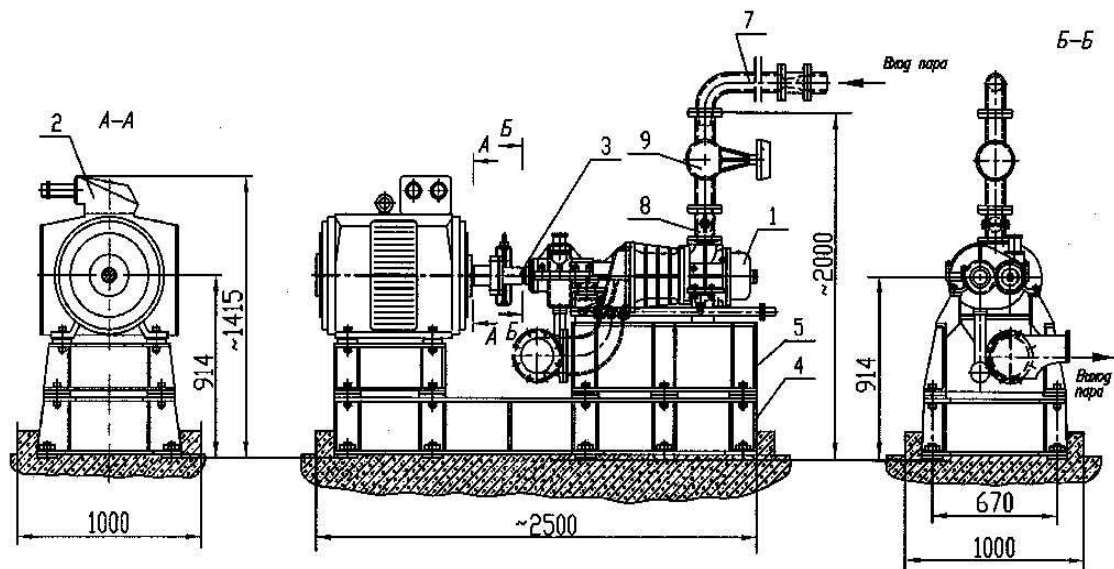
Зовнішній вид і габаритні розміри установки ПБМ-250
